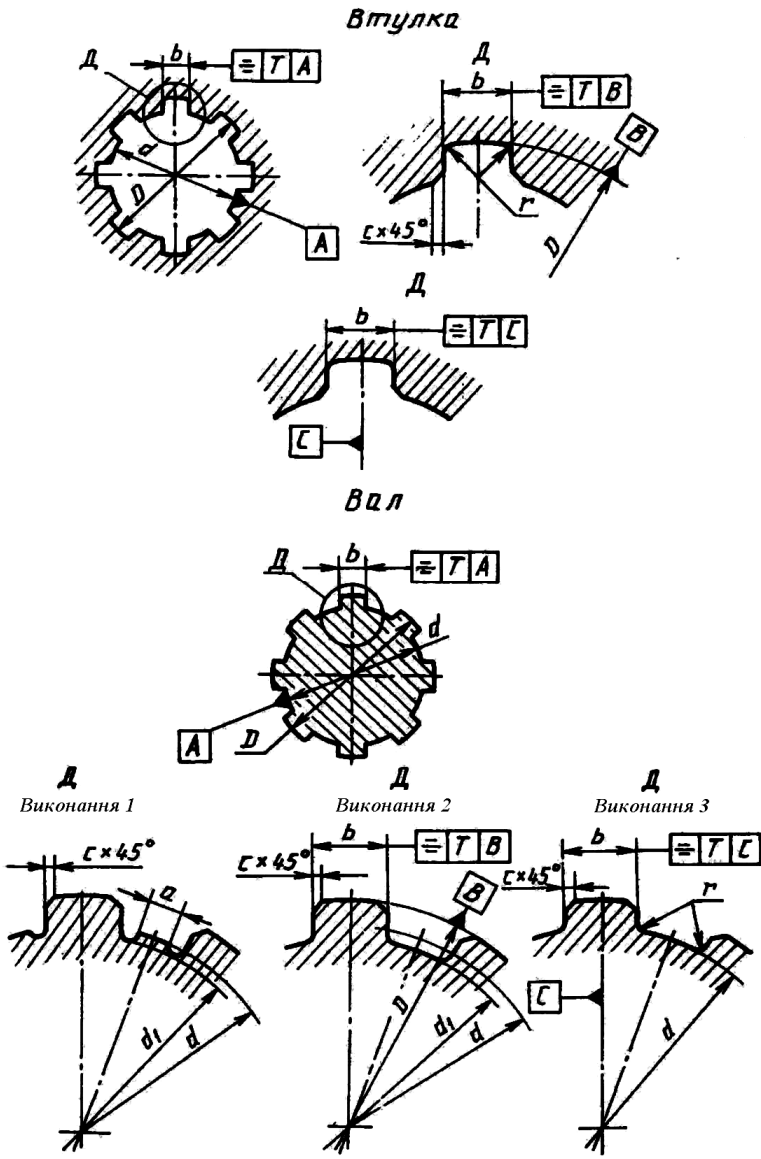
Розміри і види виконання прямобічних шліцьових деталей
